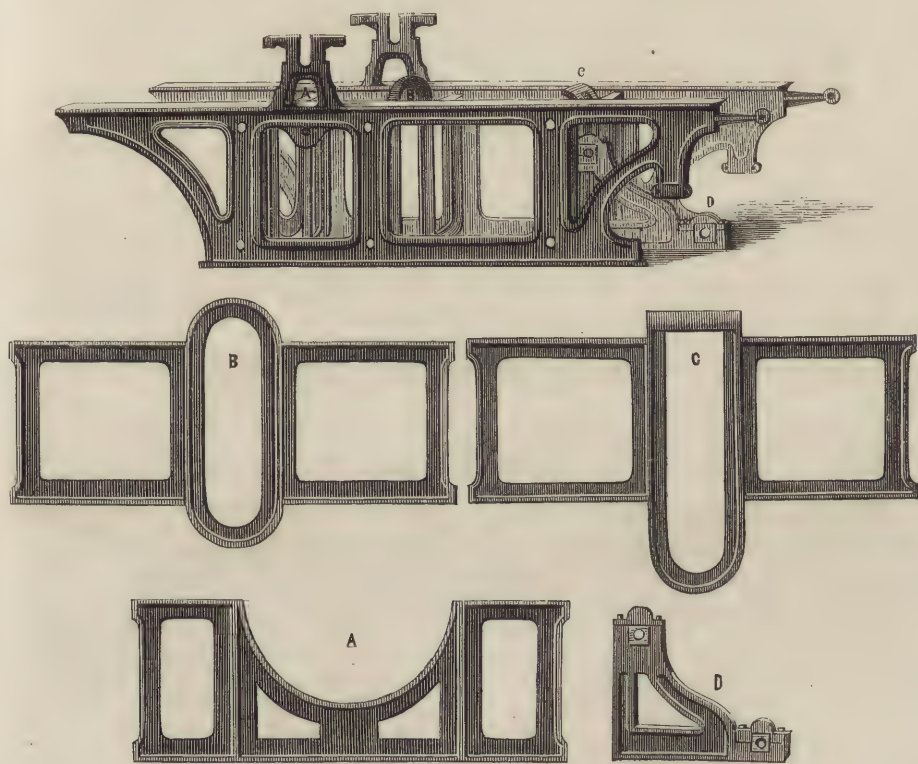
ARMATURE DE LA MACHINE EN BLANC.
